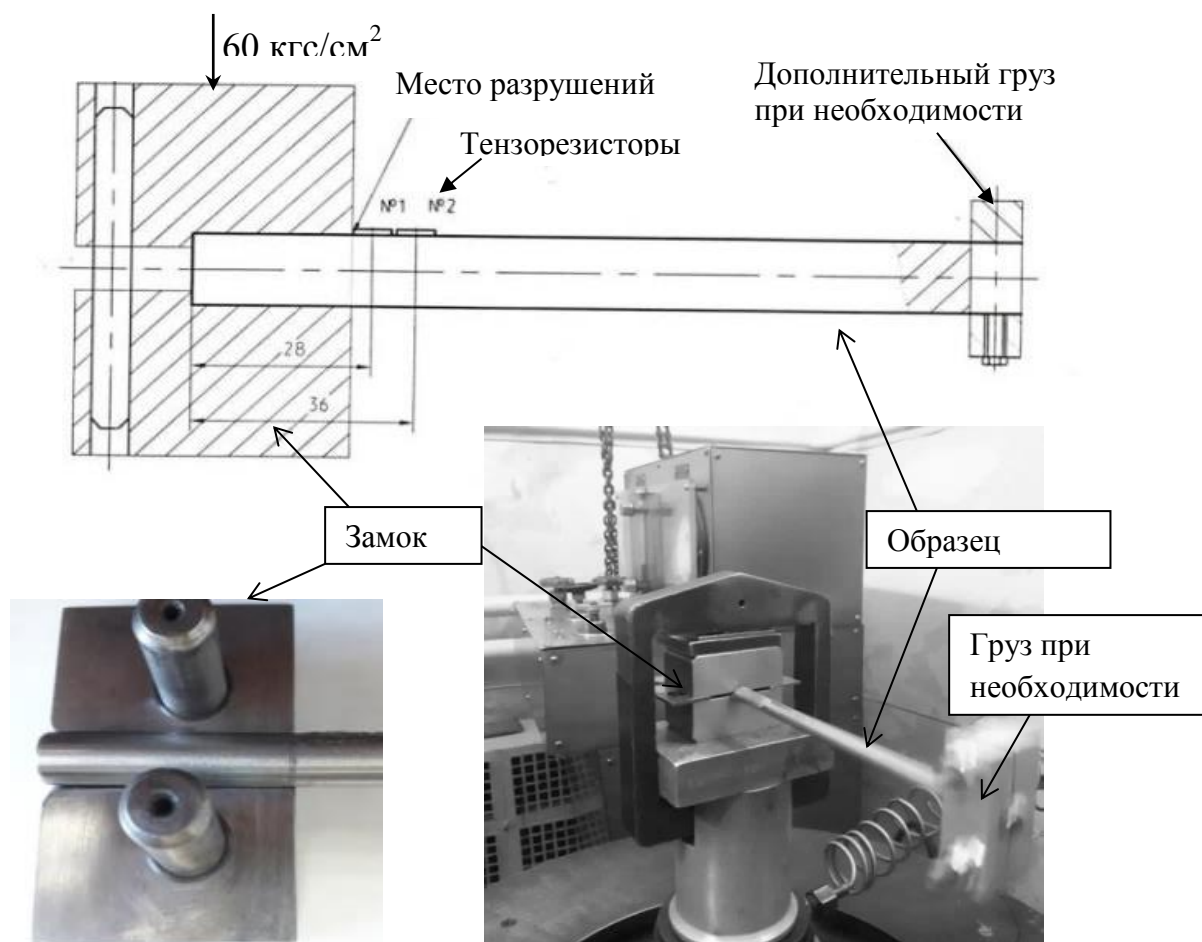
Схема испытания и крепления образца трубы и наклейки тензорезисторов на образец. База тензорезисторов 5 мм.
